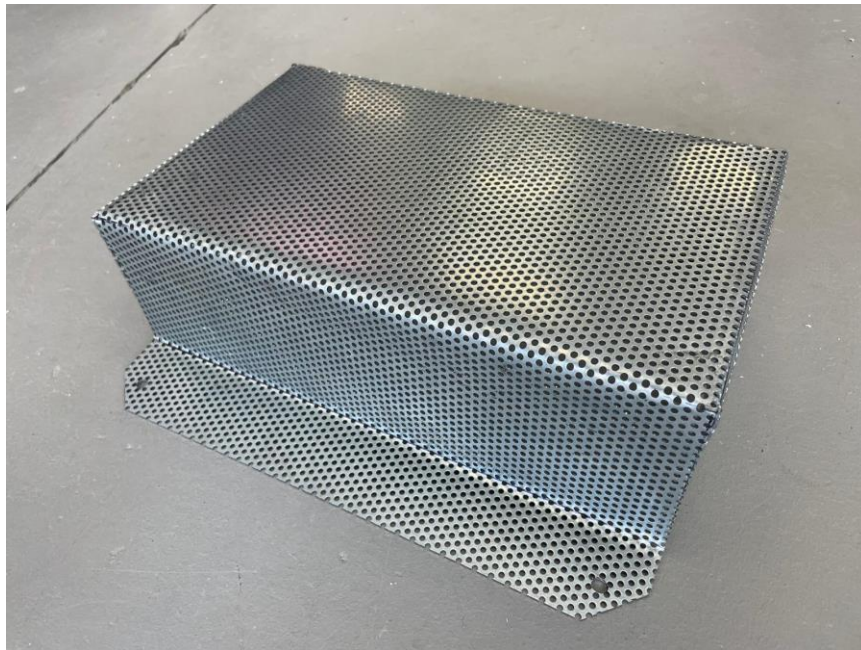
Cubierta para cajetín eléctrico (vista superior)
